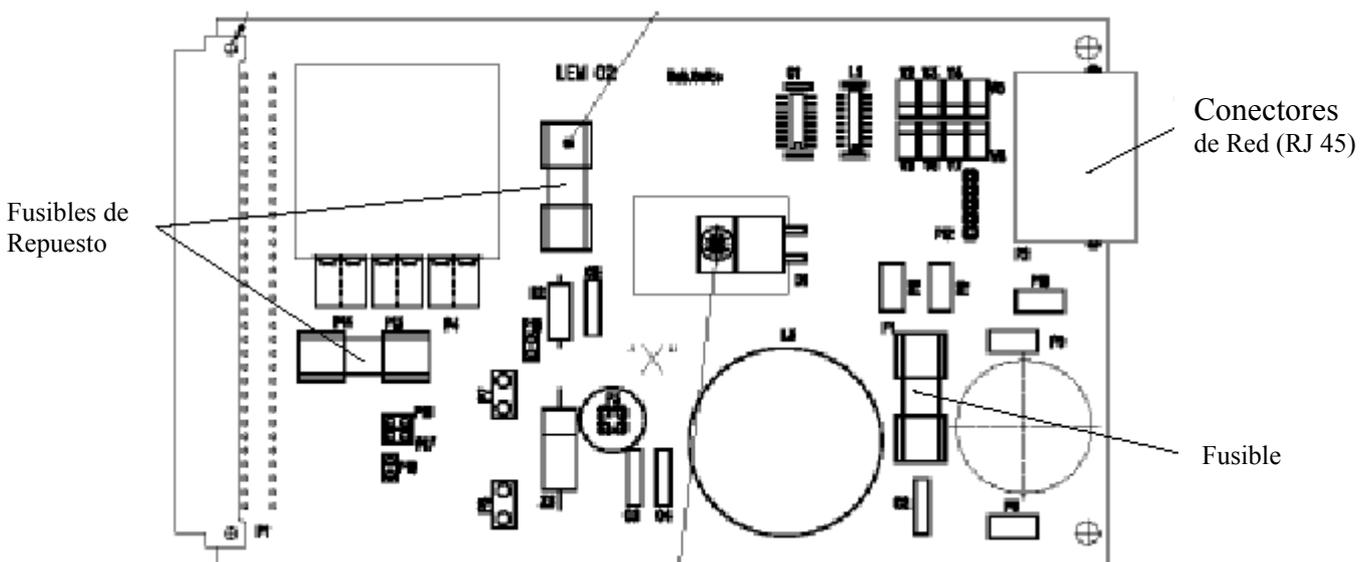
Fusibles PCB LEM 02 (lateral componentes)
